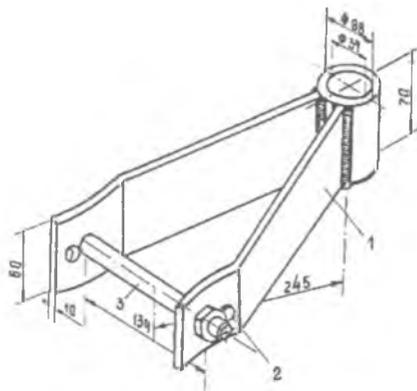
Вилка ножа: 1 - поводок вилки; 2 - болты-фиксаторы; 3 - стяжной болт
